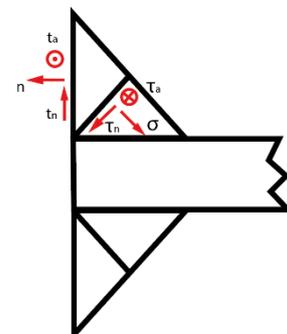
Esfuerzos internos de la soldadura
